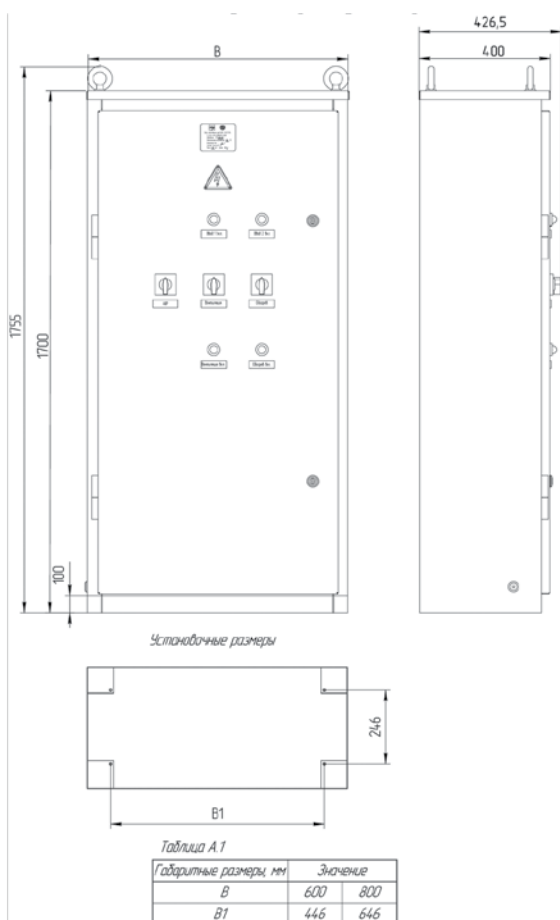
Общий вид и габаритные размеры шкафов ШСН напольного исполнения
